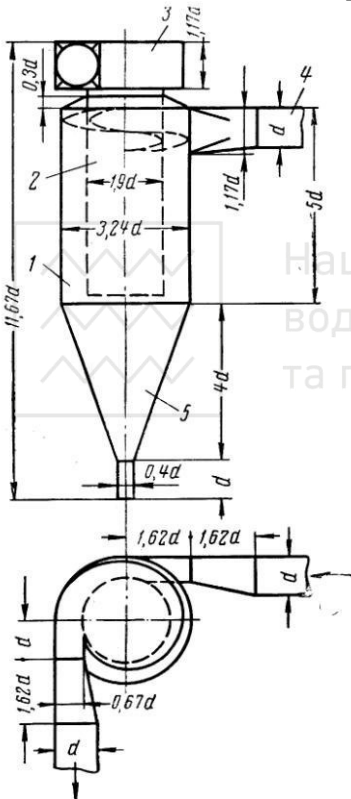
Циклон ЛІОТ: 1-циліндрична частина корпусу; 2-вихлопна труба; 3-завіток; 4-вхідний патрубок; 5-конічна частина корпусу.
